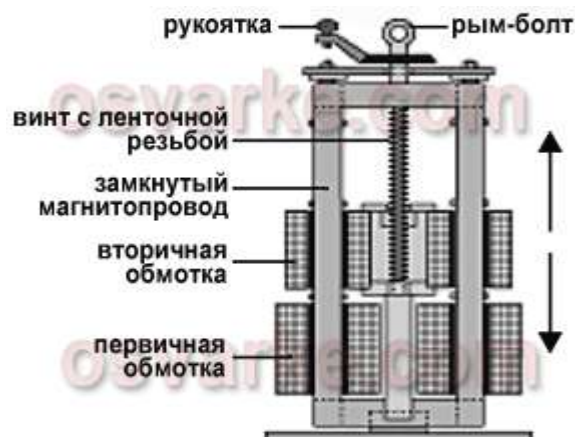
Схема регулирования тока в сварочном трансформаторе с
